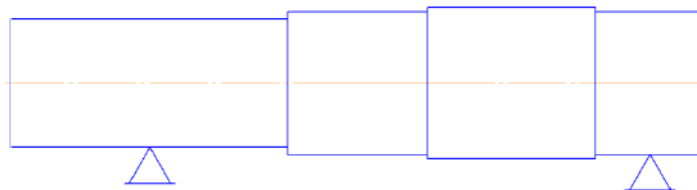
Схема установки заготовки на фрезерно-центровальном станке
